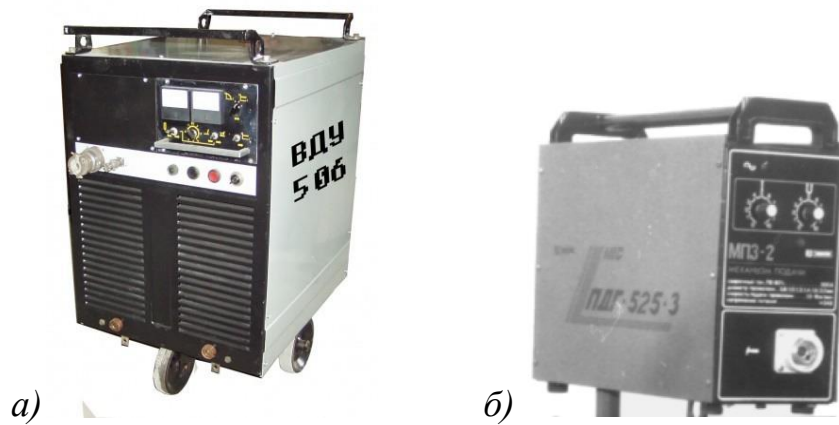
Оборудование для заварки трещины: выпрямитель дуговой сварки ВДУ-506 (а) и сварочный полуавтомат ПДГ-525 (б)
